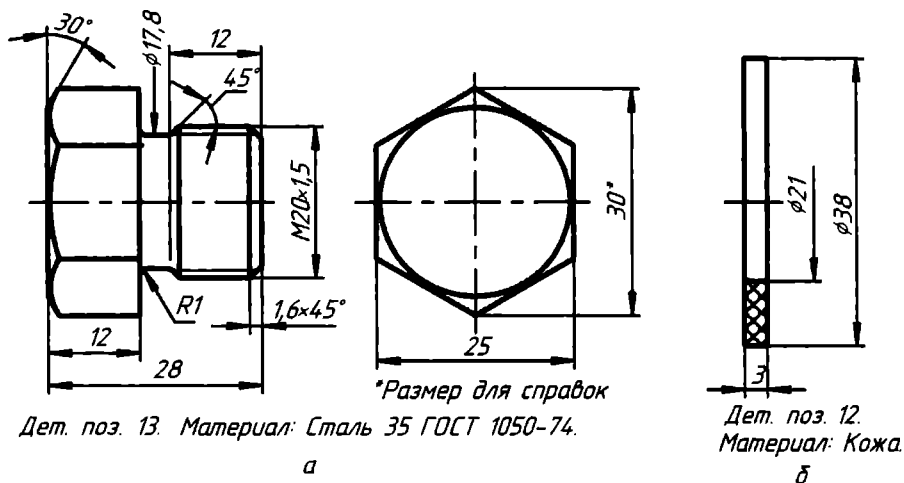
Чертежи: а — пробки; б — шайбы
